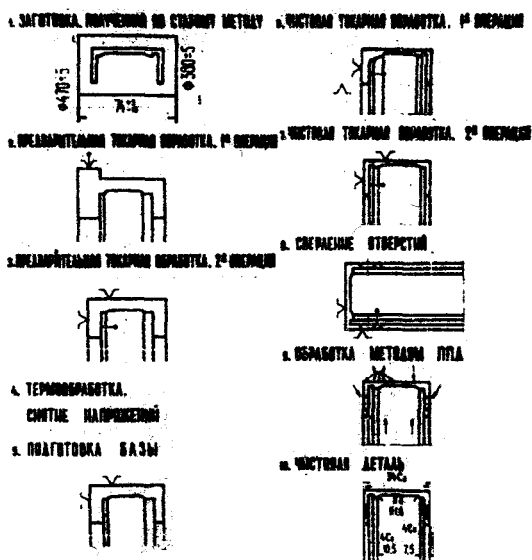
Технологическая схема изготовления промежуточного кольца диска компрессора из сплава XH68BMTЮК-ВД:
